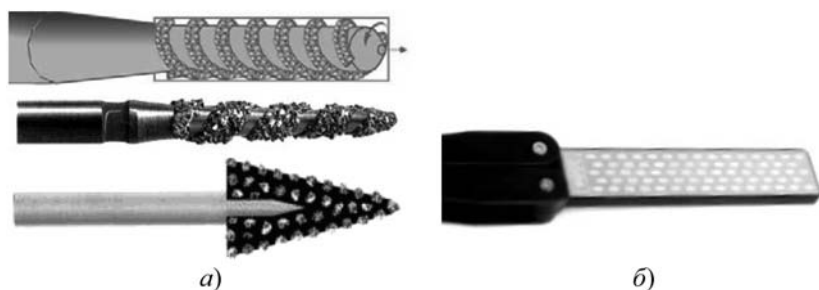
Гальванический алмазный инструмент с упорядоченным расположением режущих зерен
